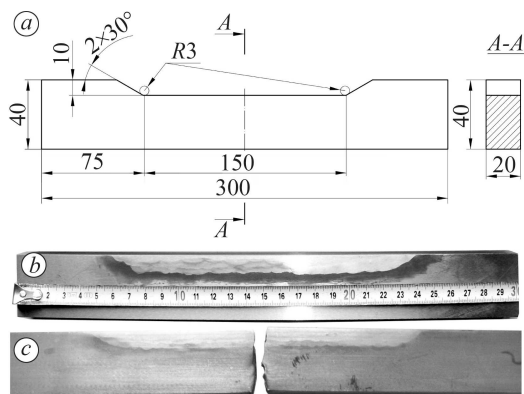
Заготовка зразка з основного металу (сталь 40Х), підготованого для наплавлення (а) та вигляд зразків перед (b) та після (c) втомних випробувань.
